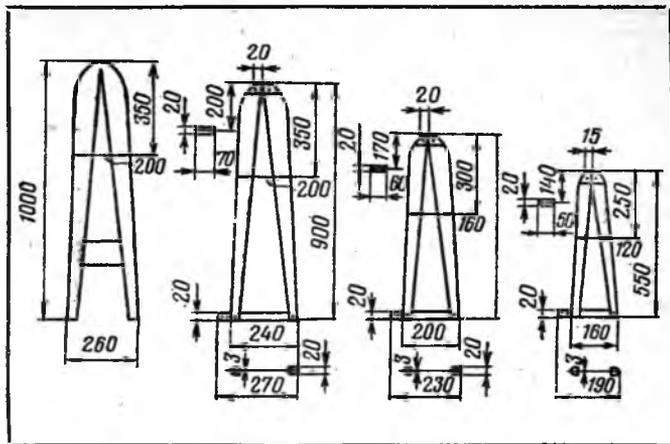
Правилки для шкурок нутрий разных размеров (мм) с закрепленными и раздвижными планками.
